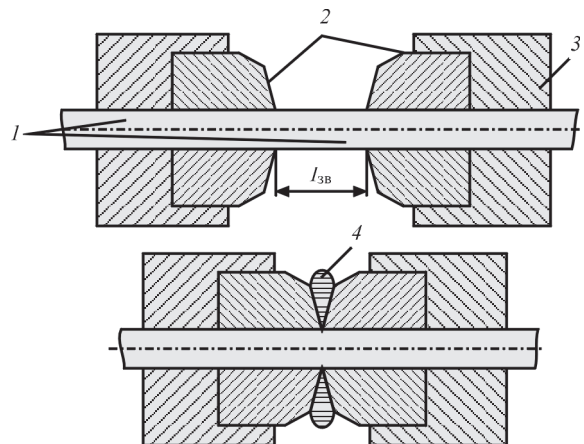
Схема КСЗО з формуванням з'єднання: 1 – деталі; 2 – формуючі пристрої; 3 – струмопідвід; 4 – екструдований метал, $l_{\text{зв}}$ – припуск на зварювання.
